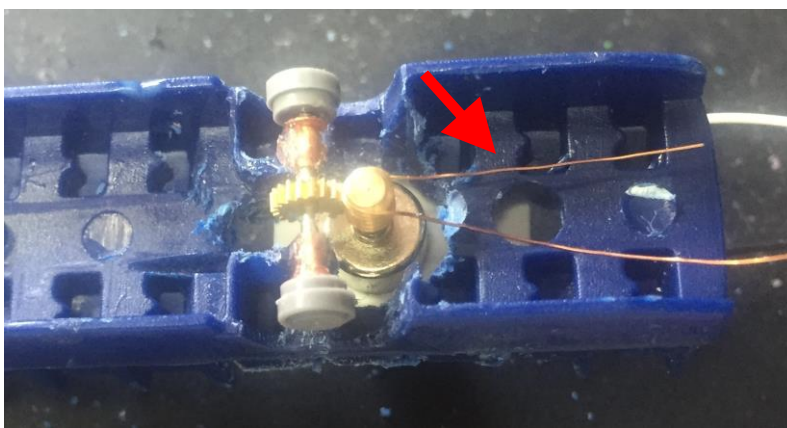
Schnecke und Zahnrad – hier mit Kupferlackdraht umwickelt zur Positionieren
